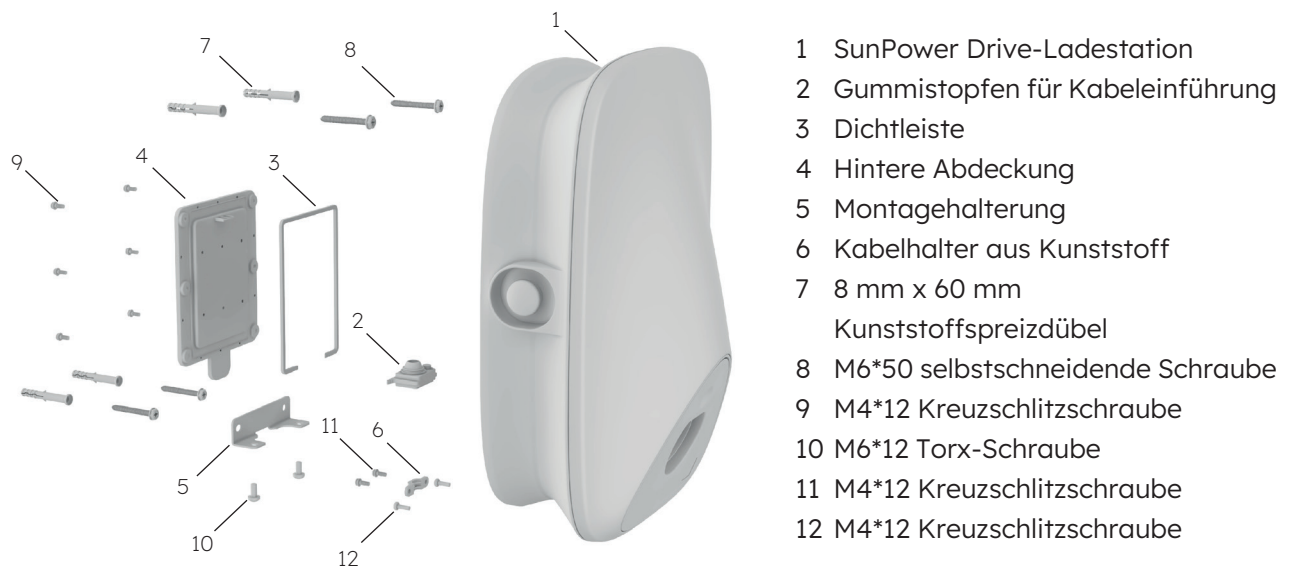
Allgemeine Montagezeichnung für die Wandmontage
